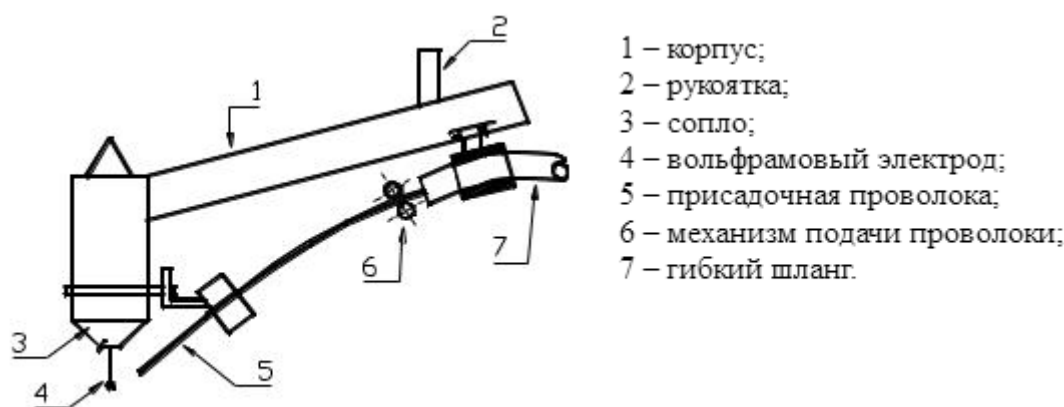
Горелка для механизированной подачи присадочной проволоки
